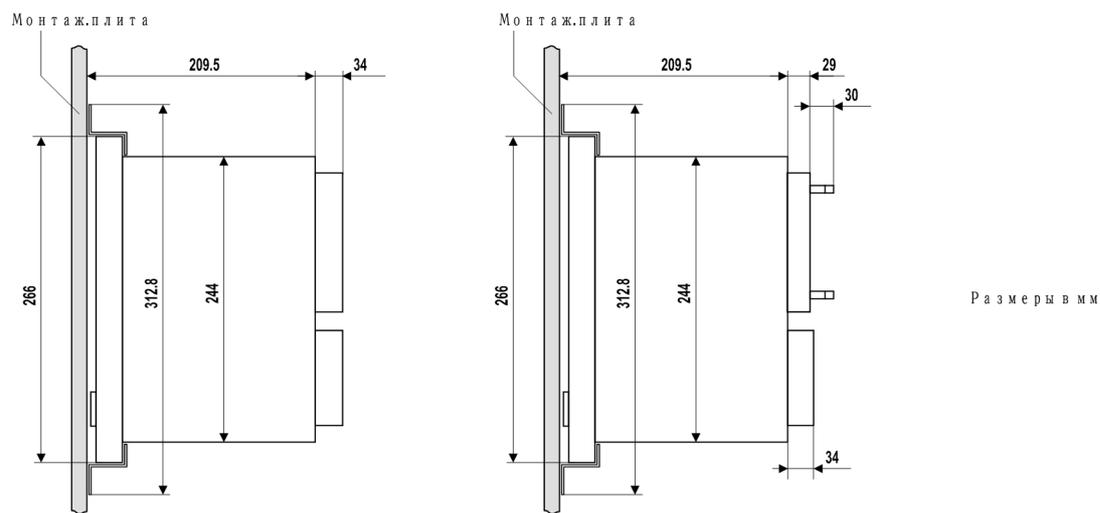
Размерный чертеж устройства 7SJ64 для монтажа с выносной панелью управления или без панели управления (размер корпуса 1/2)
